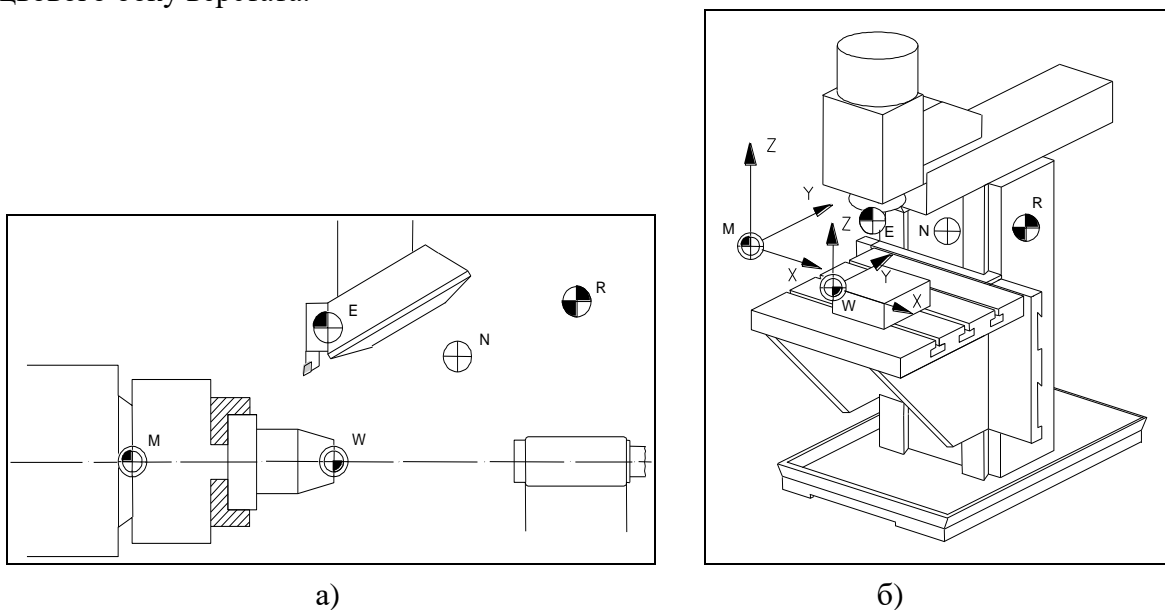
Розташування нульових точок на токарному (а) і на вертикально-фрезерному (б) верстаті з ЧПК
